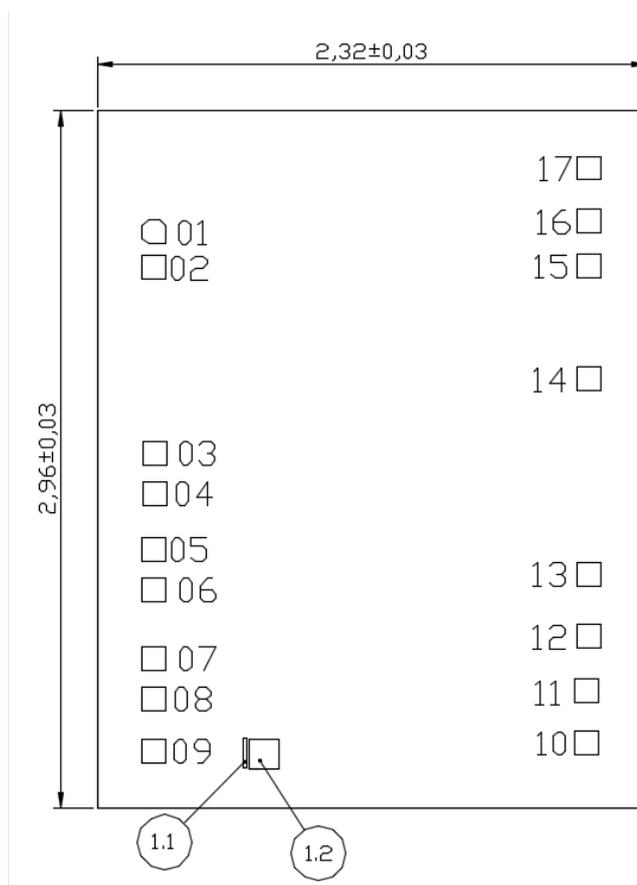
Габаритные размеры корпуса MS-013AC
